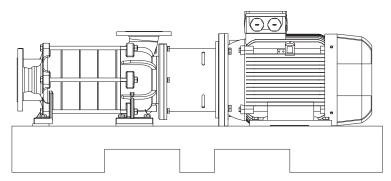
Ausbaustufe A, Pumpe mit Motor gekuppelt, mit Laterne, auf Grundplatte montiert
